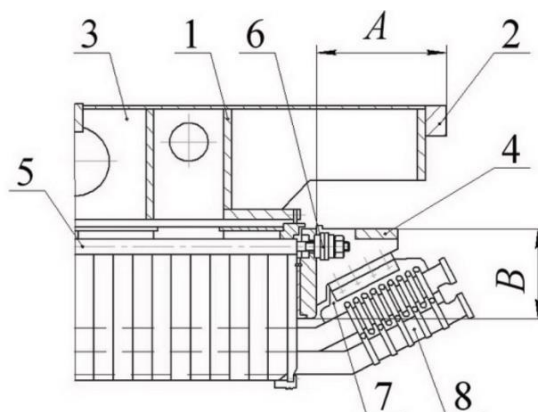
Кінцева частина статора (1 – крайня рама корпусу; 2 – фланець; 3 – стяжні ребра; 4 – натискний фланець; 5 – стяжна призма; 6 – силовий акумулятор; 7 – кронштейн; 8 – лобова частина обмотки)
